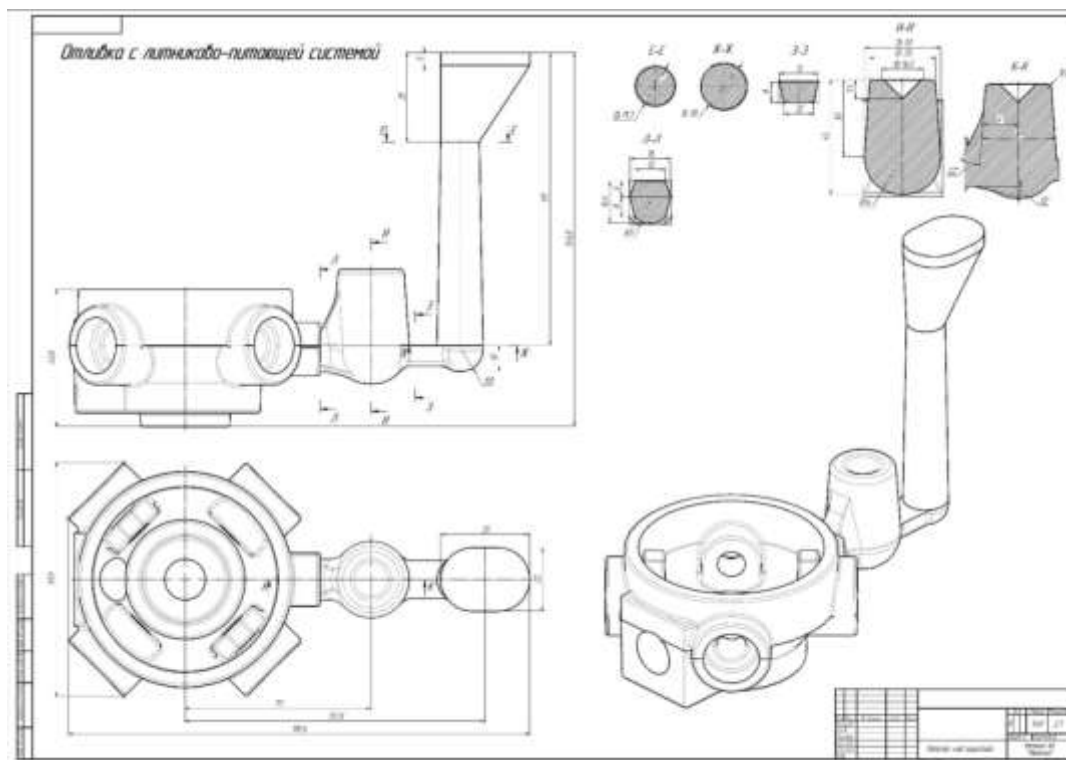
Чертеж отливки с литниково-питающей системой «Щит подшипниковый»
